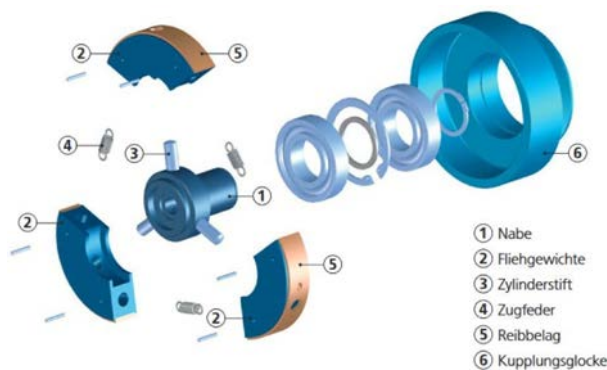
Explosionszeichnung einer Radial-Fliehkraftkupplung [10] S. 11
